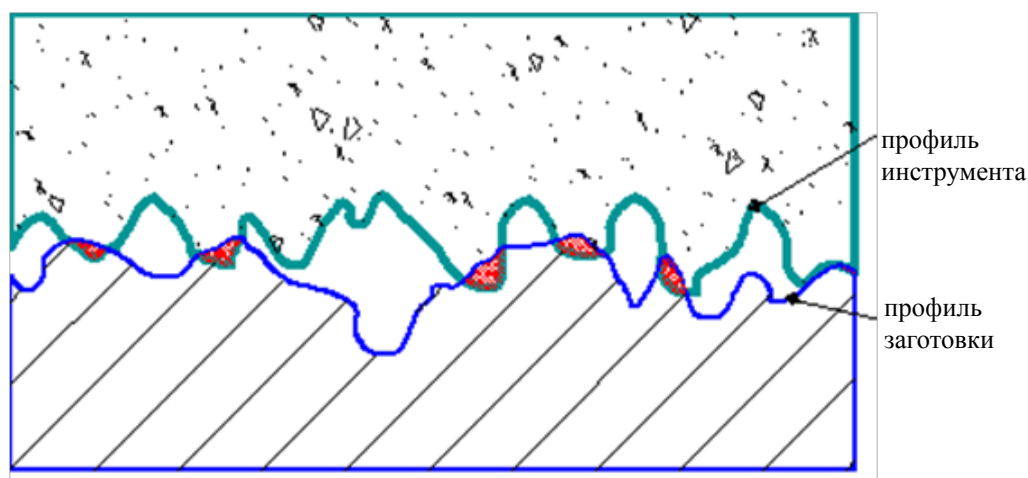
Схема взаимодействия профиля инструмента и заготовки
